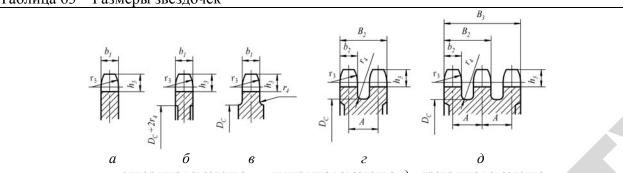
Конструкции звездочек втулочно-роликовых цепей
